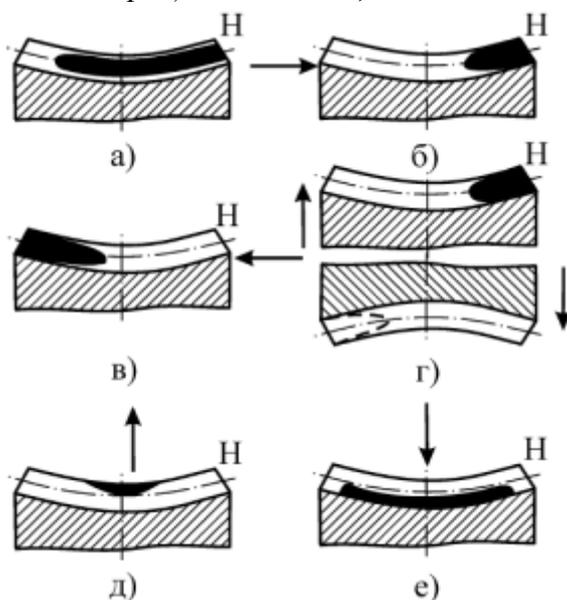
Проверка правильности установки червячного колеса относительно червяка с помощью отпечатка краски на зубьях (Н — место входа витка червяка в зубья червячного колеса): а) правильное зацепление (пятно касания располагается симметрично и занимает 70...75 % поверхности зуба); б), в) червячное колесо смещено в сторону от оси (стрелкой показано направление сдвига для устранения дефекта); г) червячное колесо перекошено; д) увеличенное межцентровое расстояние; е) уменьшенное межцентровое расстояние
